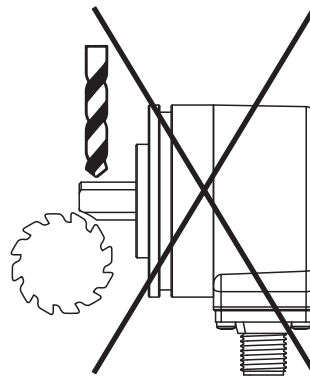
Montageansicht – nicht nachträglich bearbeiten
